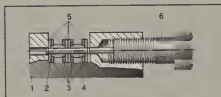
Приспособление для выпрессовки пальца цепи: 1 — скоба; 2 — палец цепи; 3 — внутренние пластины; 4 — втулка; 5 — наружные пластины; 6 — болт-выталкиватель.
